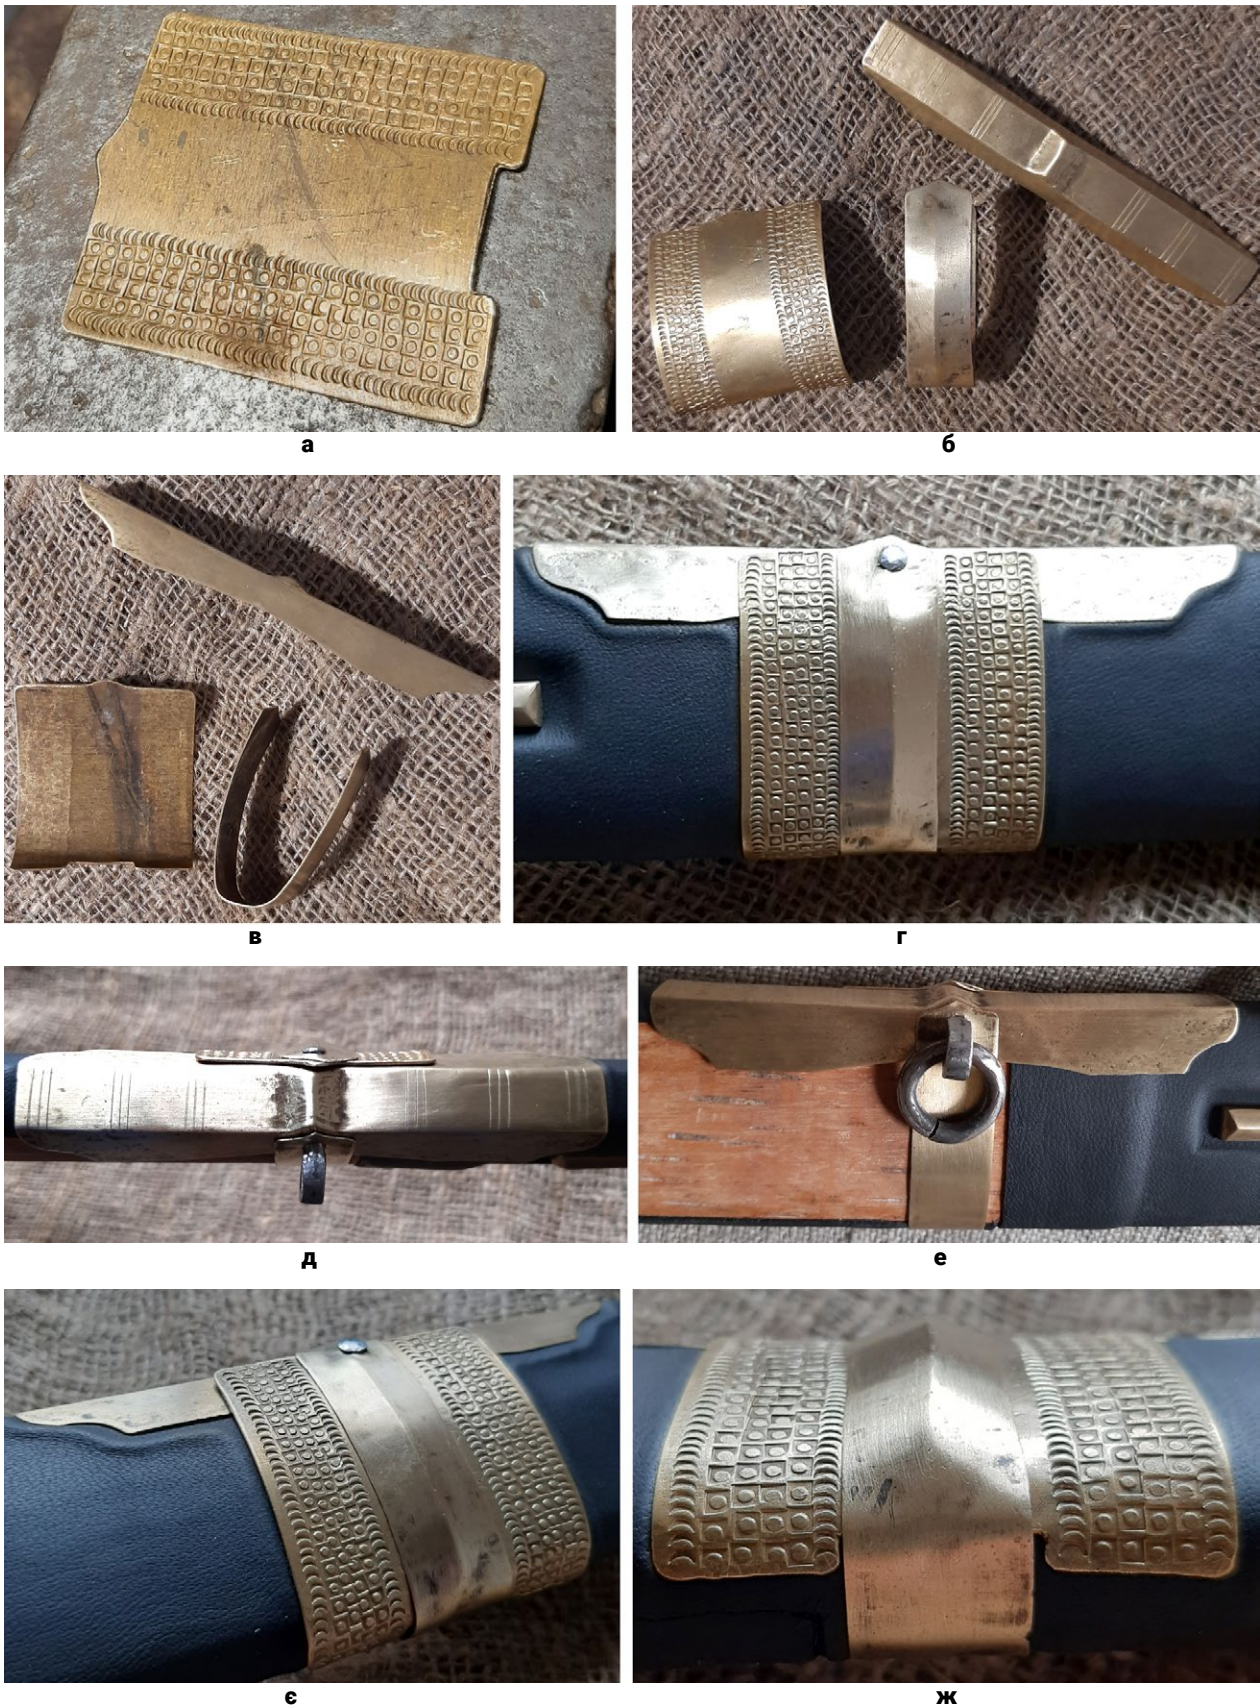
Деталі виготовлення піхов: (а) – підрізка устя під форму перехрестя;
